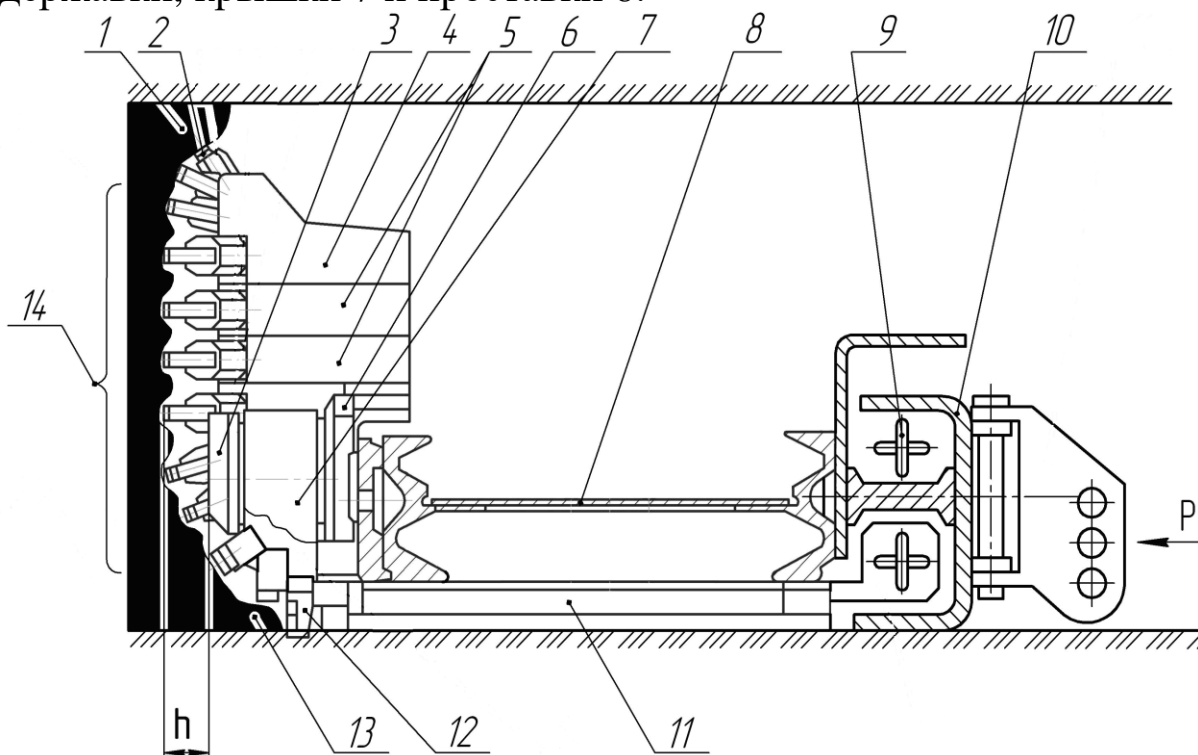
Разрез по корпусу исполнительного органа струговой установки 2СО3413 отрывного типа:
